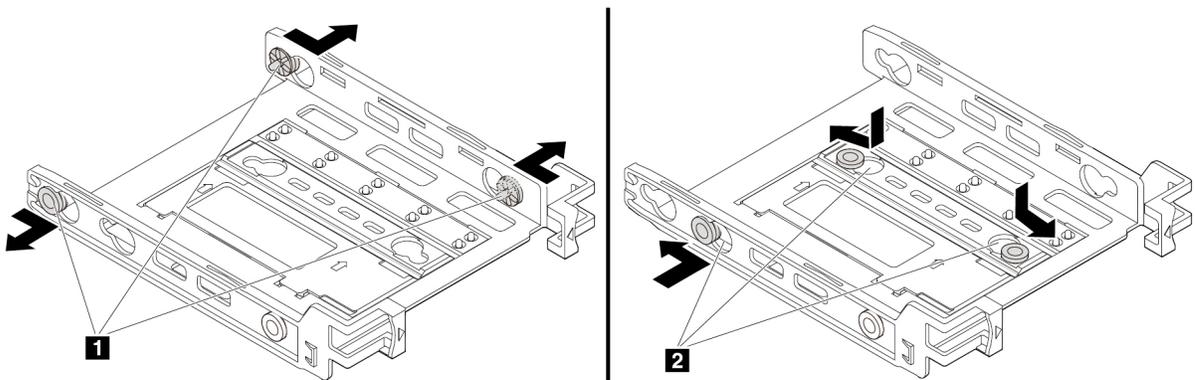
Extracción de patillas y reinstalación de estas en las nuevas ranuras
